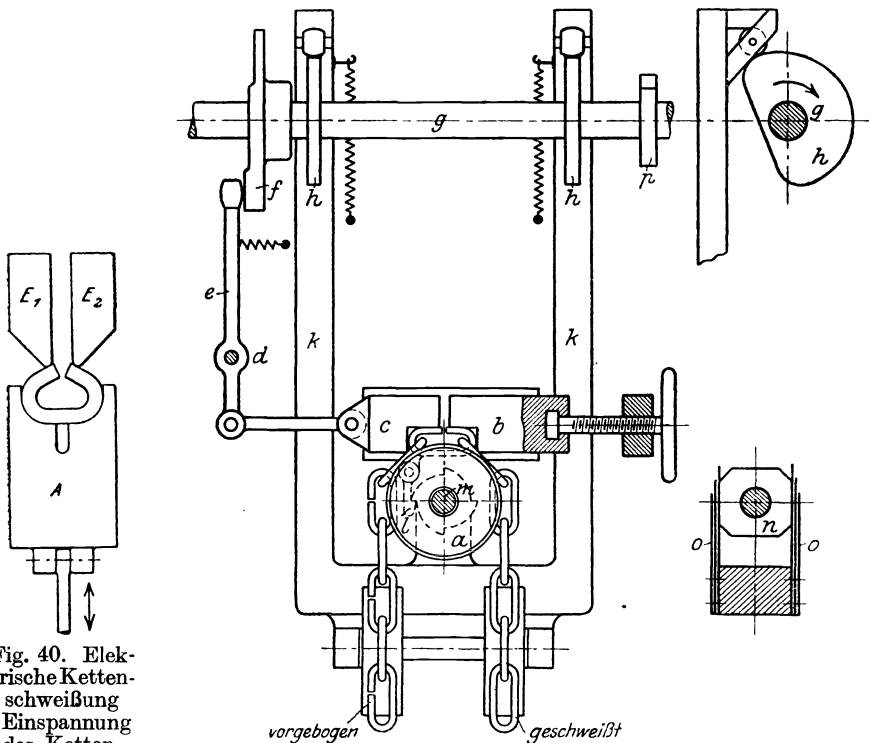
Schema einer selbsttätigen elektrischen Kettenschweißmaschine.
